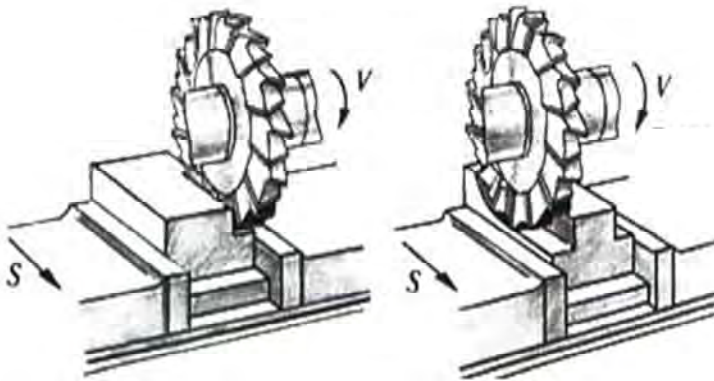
Фрезерование 2-х уступов трехсторонней дисковой фрезой
